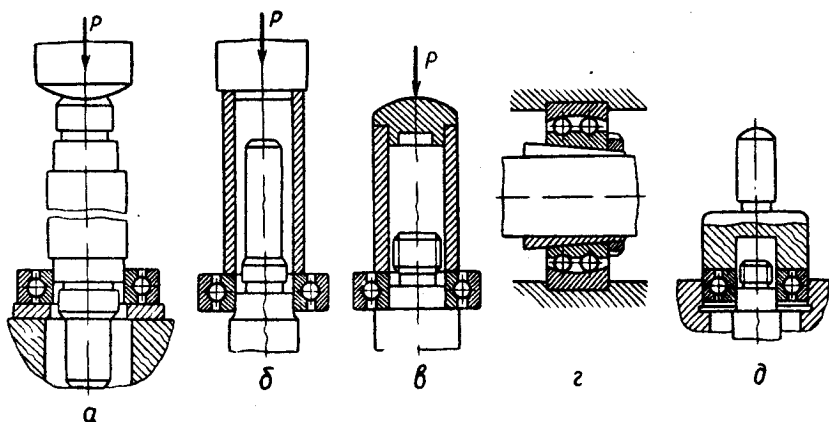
Встановлення підшипників кочення на вал і в корпус деталі
